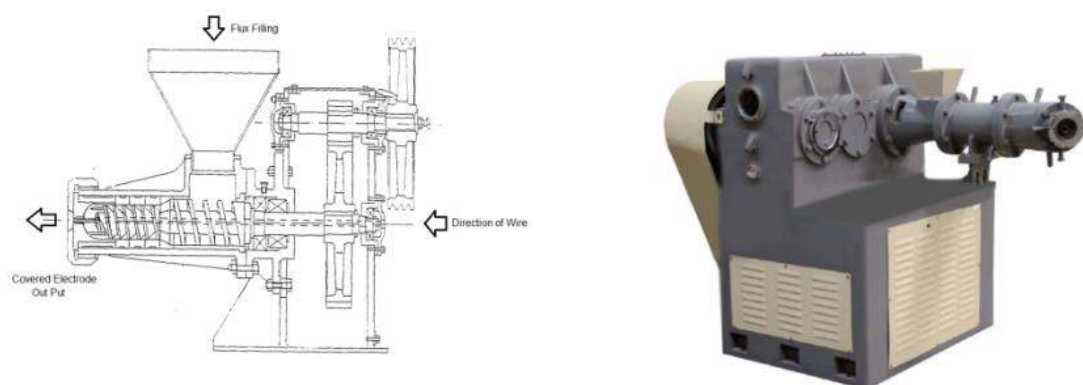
Máquina de recubrimiento por tornillo sin fin.
